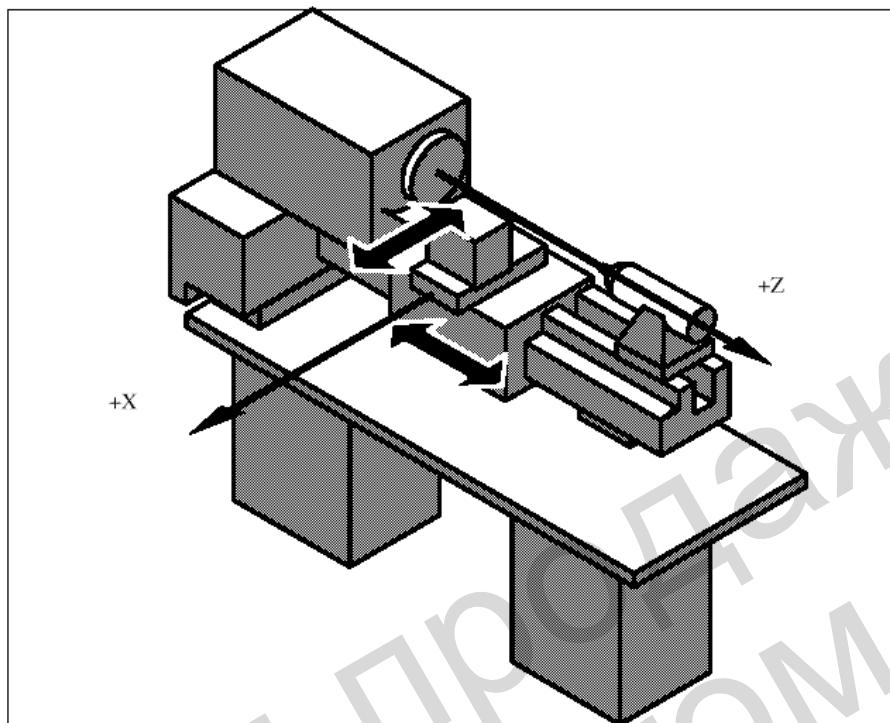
Координаты/оси станка на примере токарного станка
